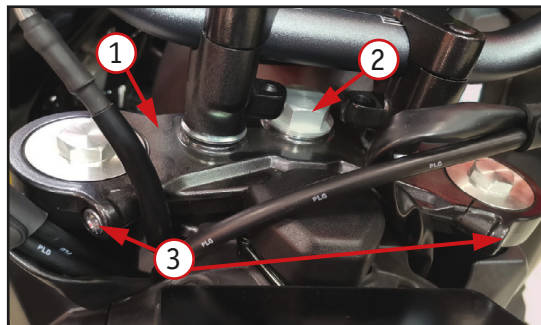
Регулировка подшипников рулевой колонки: 1 – верхняя траверса; 2 – верхняя защитная гайка; 3 – винт крепления пера к верхней траверсе.
